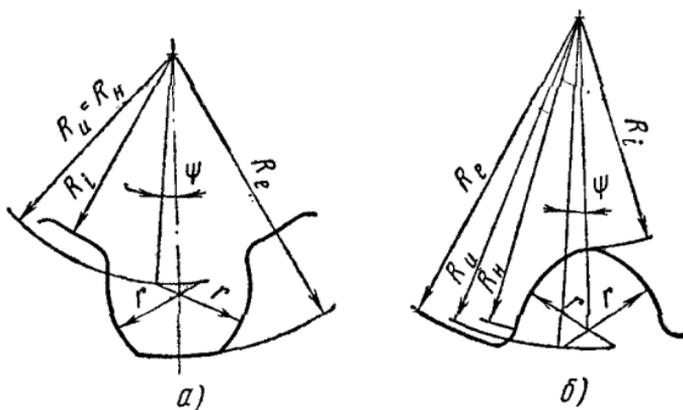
Профиль зубчатых колес М. Л. Новикова:
